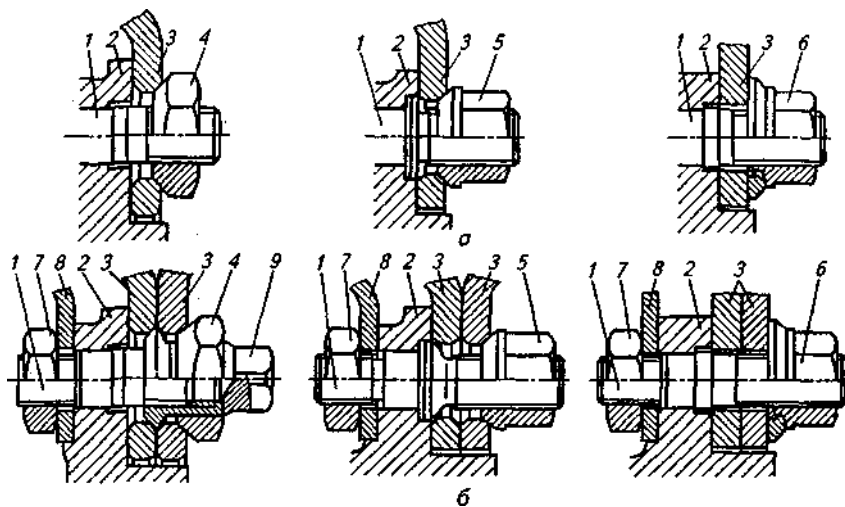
Крепление дисковых колес грузовых автомобилей: *а* — одинарных; *б* — сдвоенных; 1 — шпилька; 2 — ступица; 3 — диск; 4 — гайка крепления наружного диска; 5 — гайка типа ДИН; 6 — гайка с завальцованной шайбой; 7 — гайка крепления тормозного барабана; 8 — тормозной барабан; 9 — гайка крепления внутреннего диска
